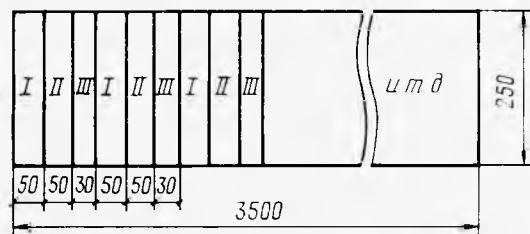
Схема выпилки образцов для проведения сравнительных испытаний
